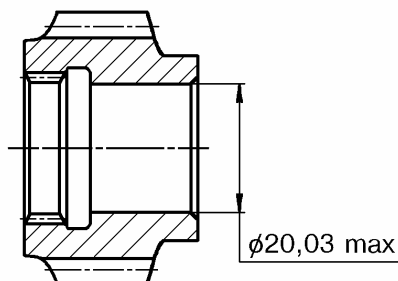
Шестерня заднего хода промежуточного вала 2101-1701138.
